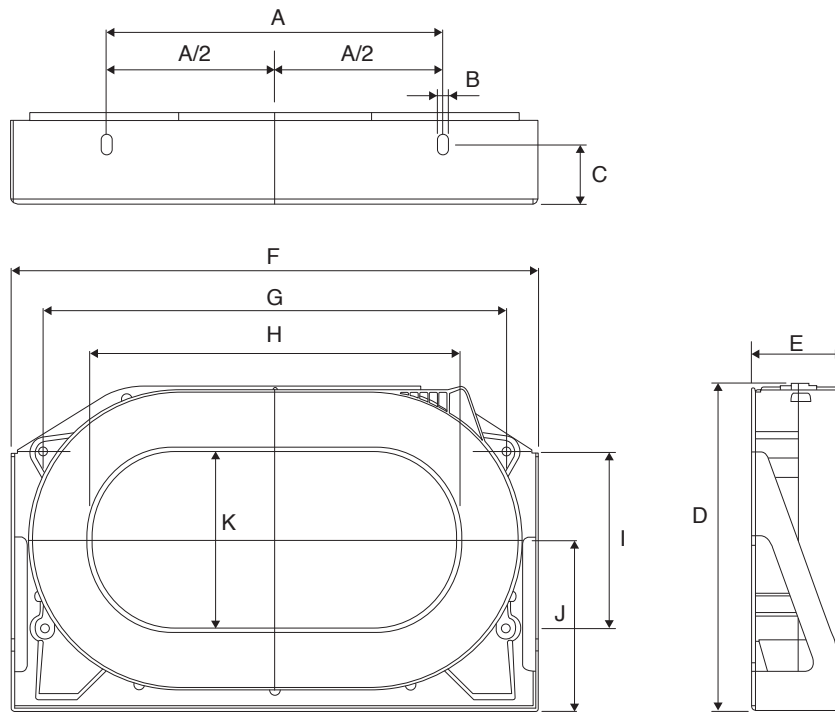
Dimensiones WGC 220x105, WGC 350x150 y WGC 500x200 (en mm).
